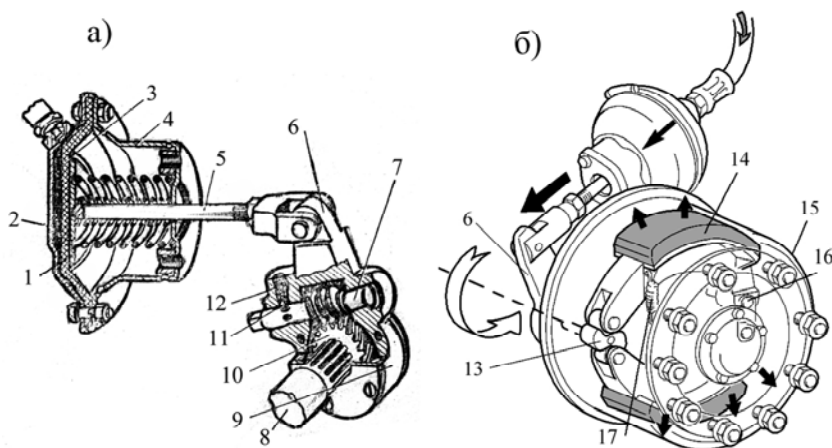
Тормозная камера, привод разжимного кулачка (а) и барабанный тормозной механизм (б):
